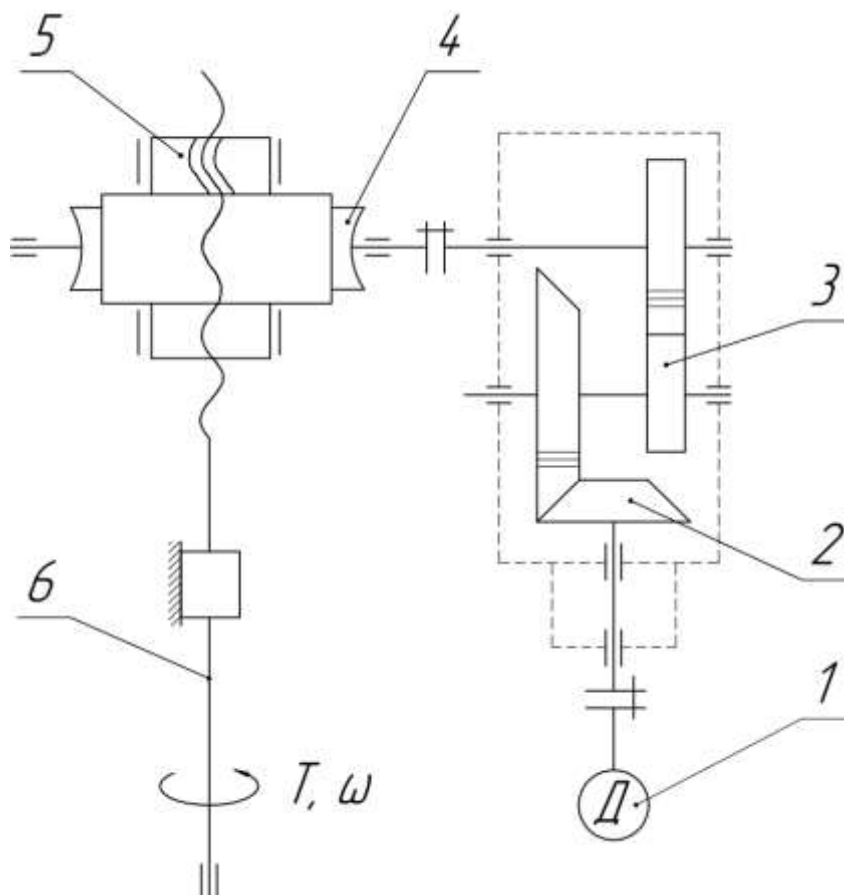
Кінематична схема приводу: 1- двигун, 2 – циліндрична прямозуба передачі; 3 – черв'ячна передача; 4 – черв'ячна передача; 5 – гвинт.
